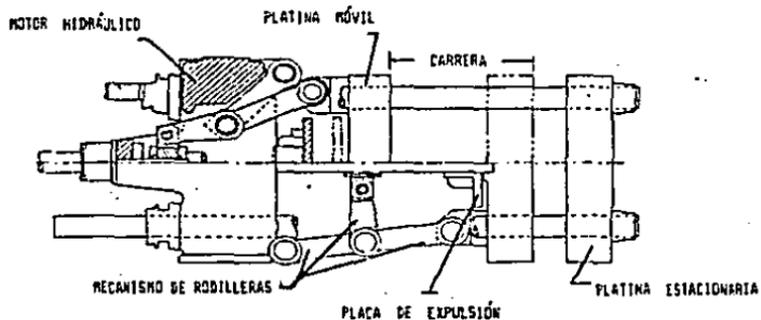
Unidad de cierre de una máquina de moldeo de materiales termoplásticos por inyección con sistema mecánico.
